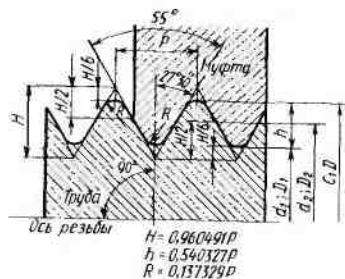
Профиль трубной цилиндрической резьбы:
